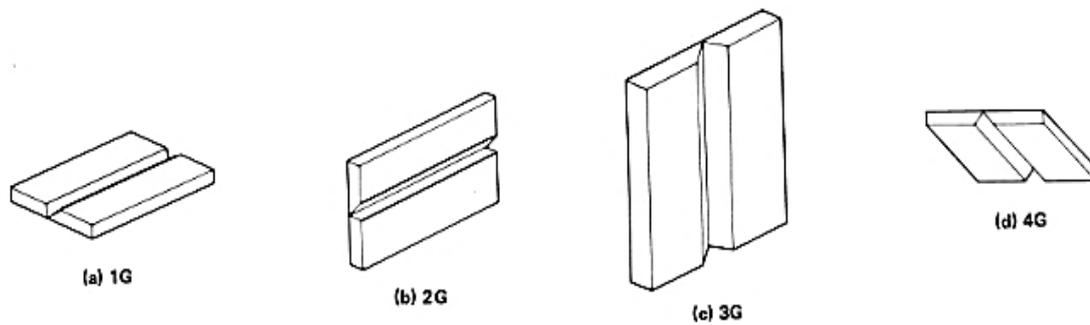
Posiciones de soldadura para placas en ranura.
